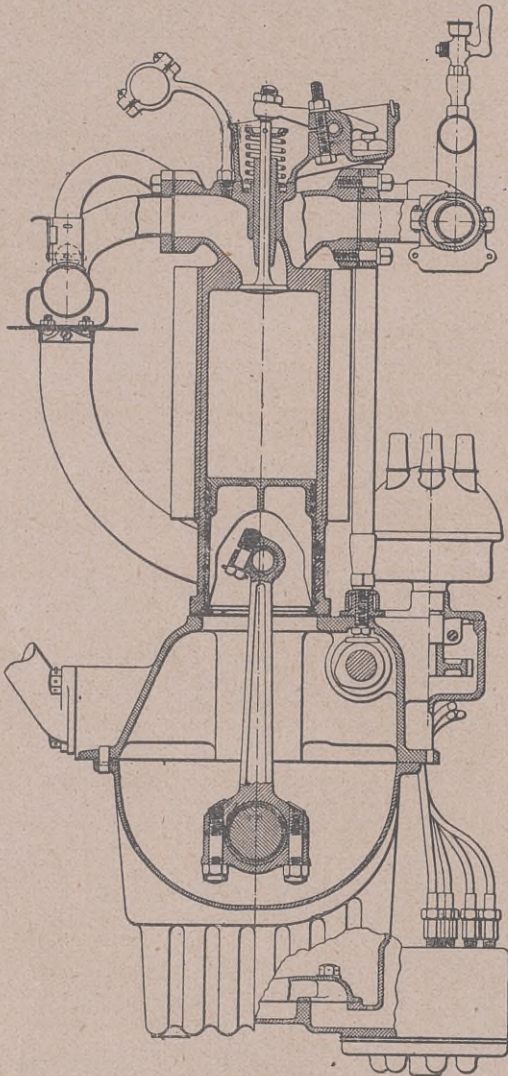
Querschnitt des luftgekühlten Verbrennungsmotors.
